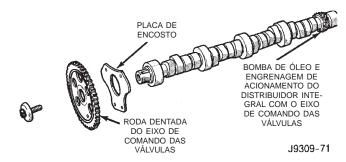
Conjunto do Eixo de Comando de Válvulas e Roda Dentada
